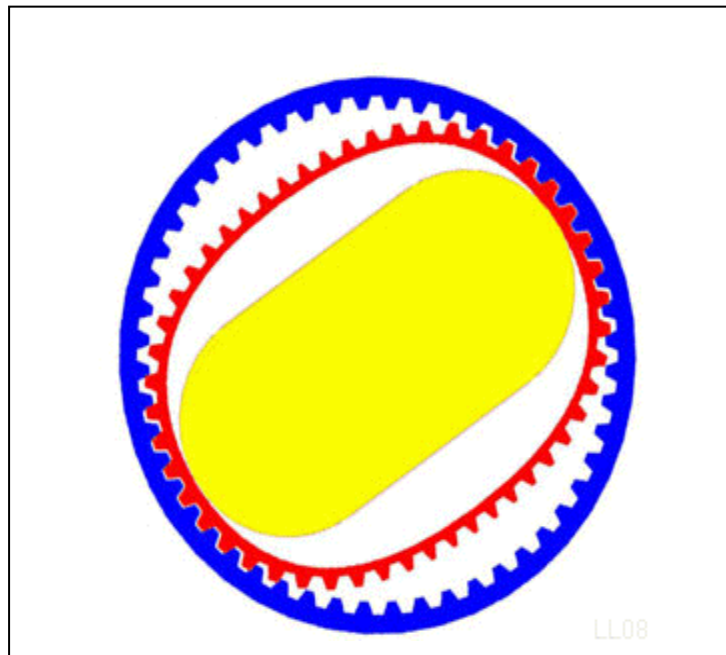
Engranaje de manejo armónico o engranaje de onda de tensión
